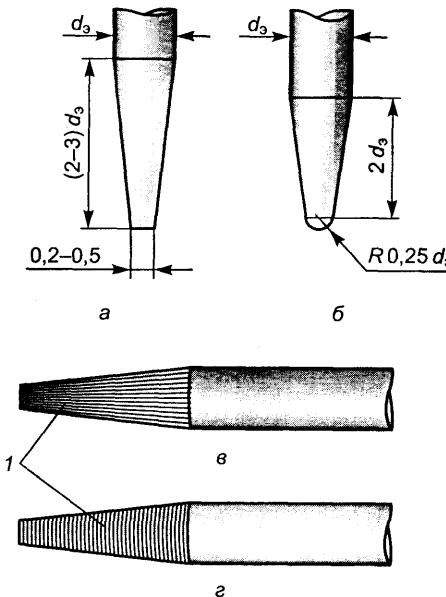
Заточка вольфрамовых электродов для сварки:
